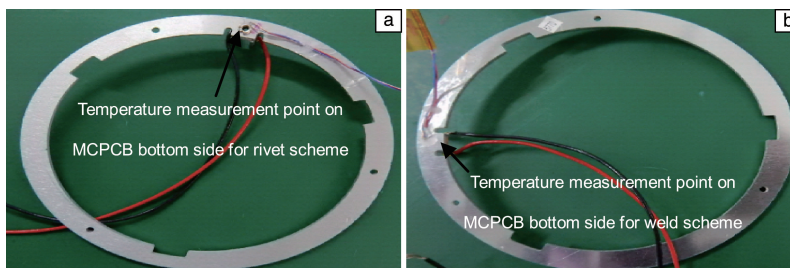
天使眼 LED 灯 MCPCB 底部温度测试：MCPCB 铆接方案(a)和 MCPCB 焊接方案(b)测温点
